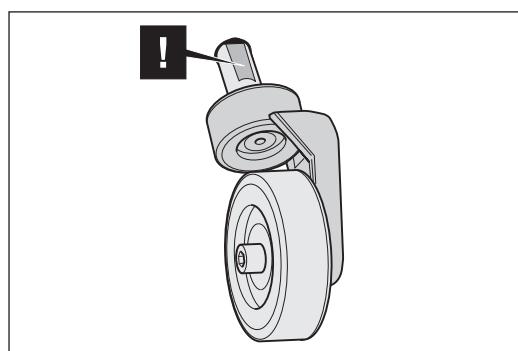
Beim Einbau des Hinterrades in die Maschine die Fläche der Spornachse zur Schraube im Maschinengehäuse ausrichten.
